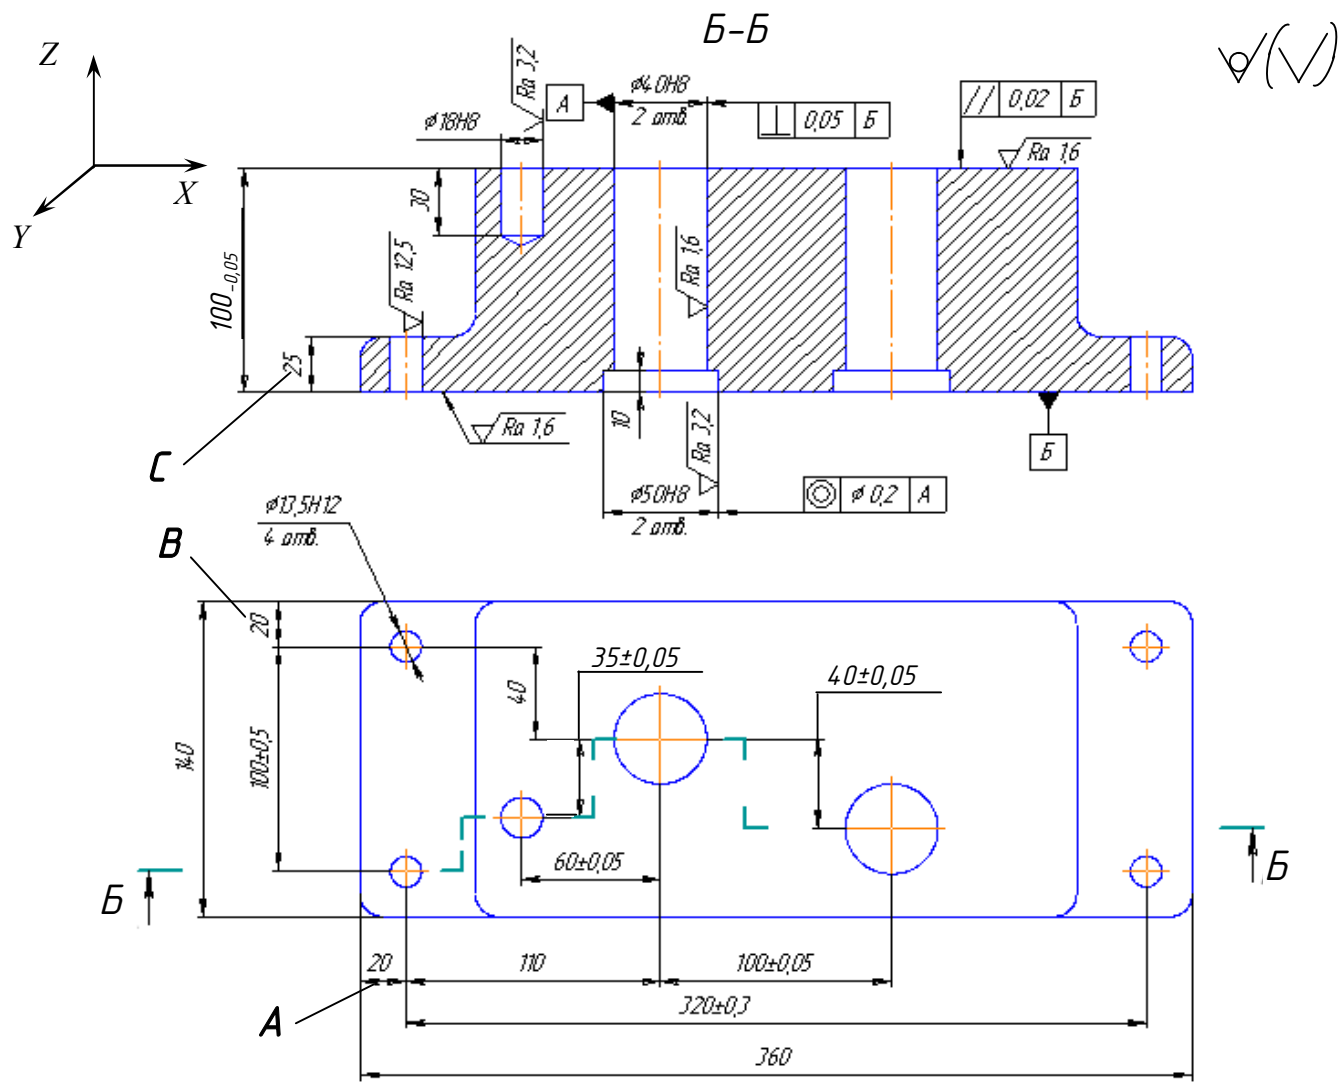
Приклад розтушування розмірів на кресленні деталі, яка має оброблені й необроблені поверхні (заготовка — вилівок)
